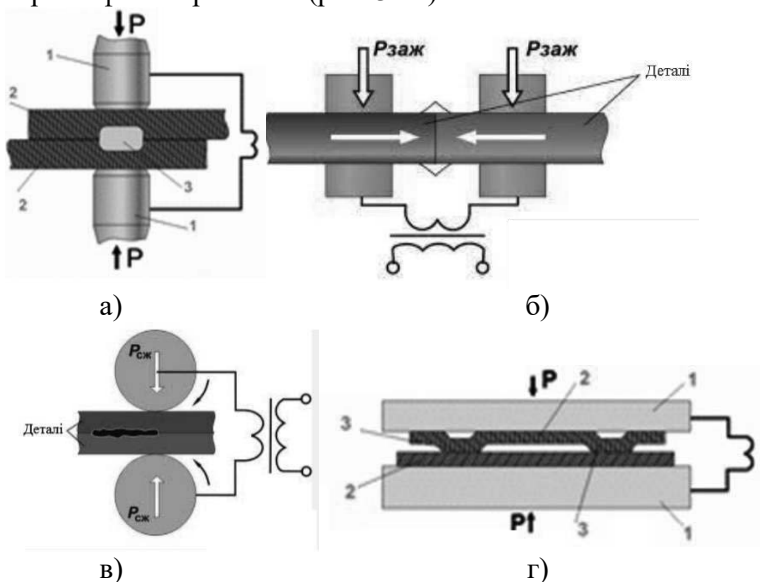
Схеми контактного зварювання: а – точкове; б – стикове; в – шовне; г – рельєфне; 1 – контактні плити; 2 – деталі, що зварюються; 3 – рельєфи; 4 – зварювальні точки
